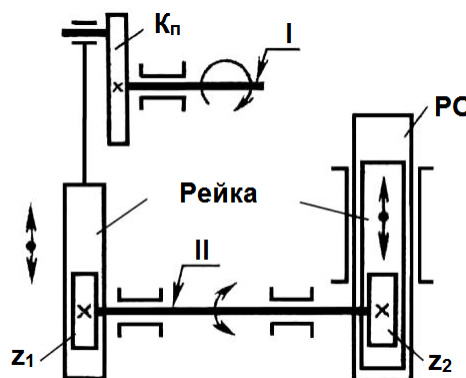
Подвійний кривошипно-рейковий механізм
